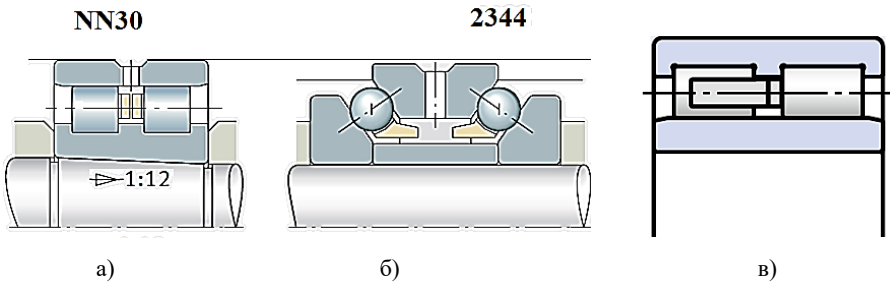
Схема установки підшипників в передній опорі шпинделя
